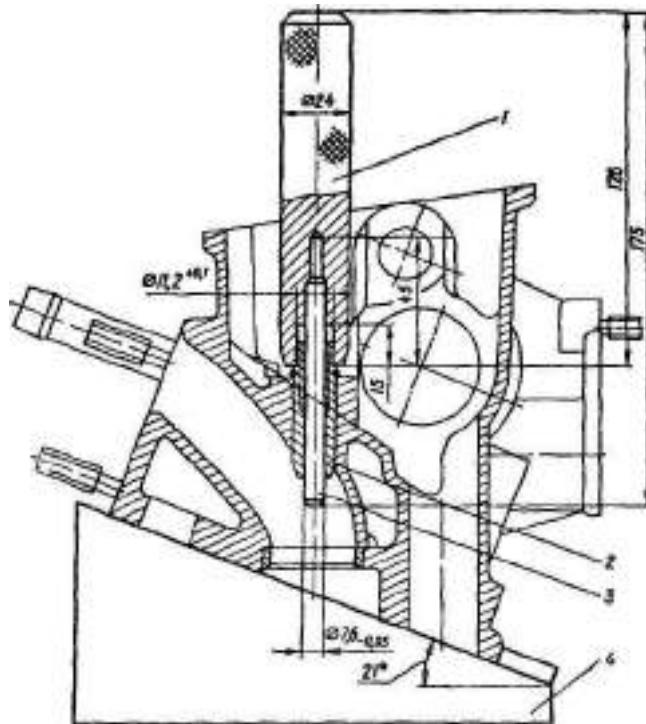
Оправка для випресування прямої втулки клапана:
